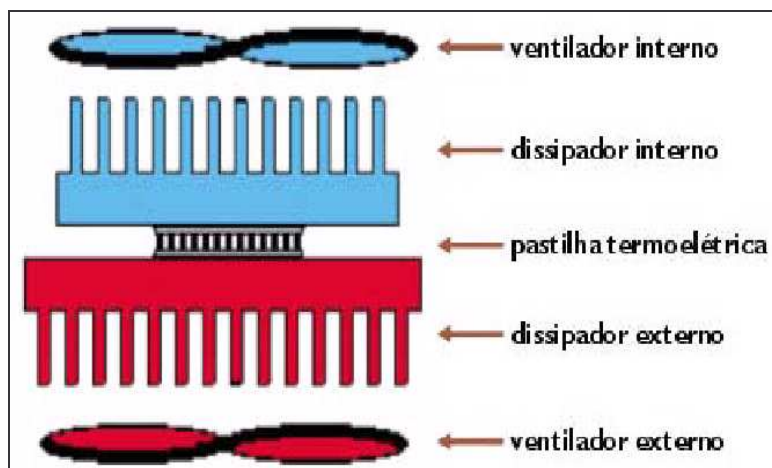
Detalhe da montagem do conjunto módulo termoeletrico e dissipadores
